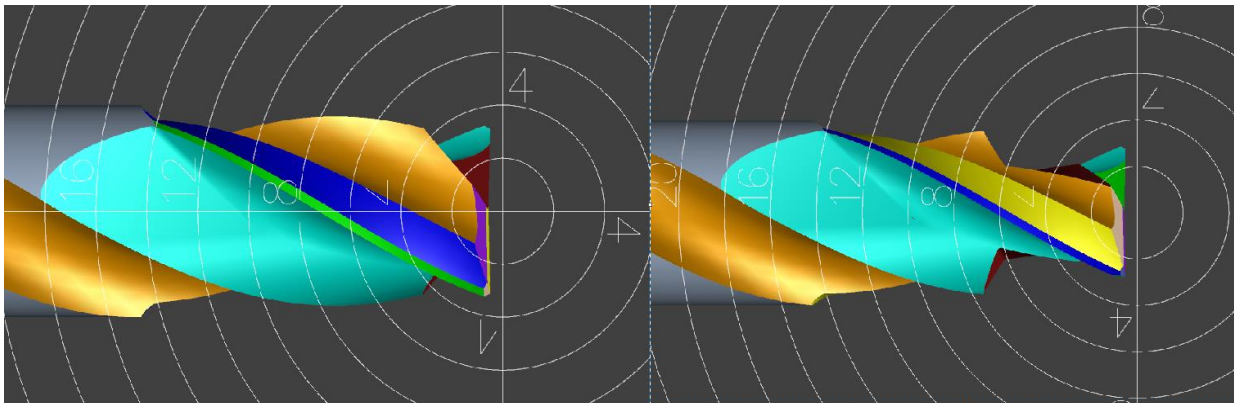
Inovovaná verze frézy / Výchozí fréza
